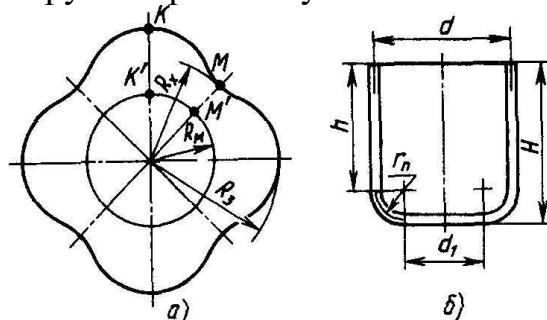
Фигурная (профильная) заготовка (а) для получения деталей без
